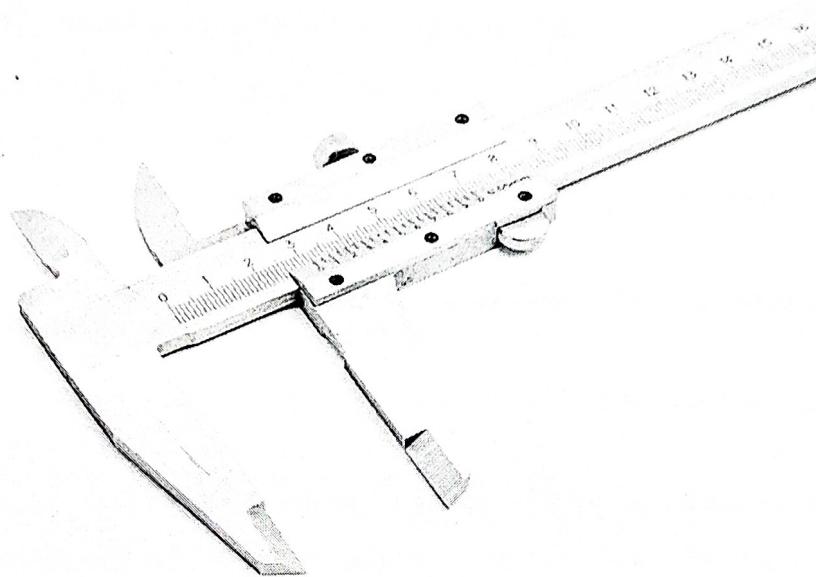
Штангенциркуль (ШЦ-1-250 0.05)
